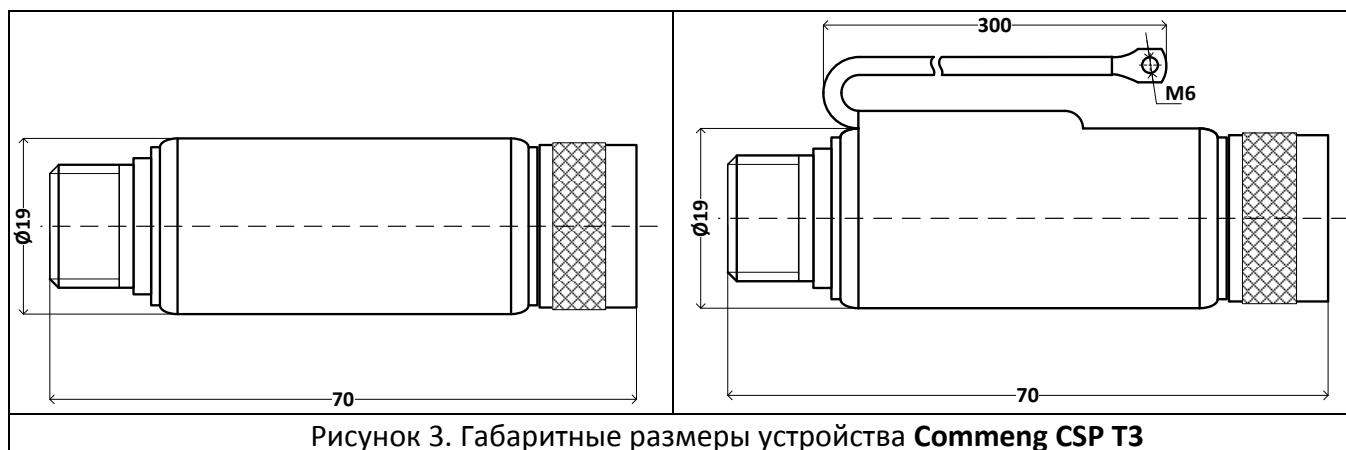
Габаритные размеры устройства Commeng CSP T3
